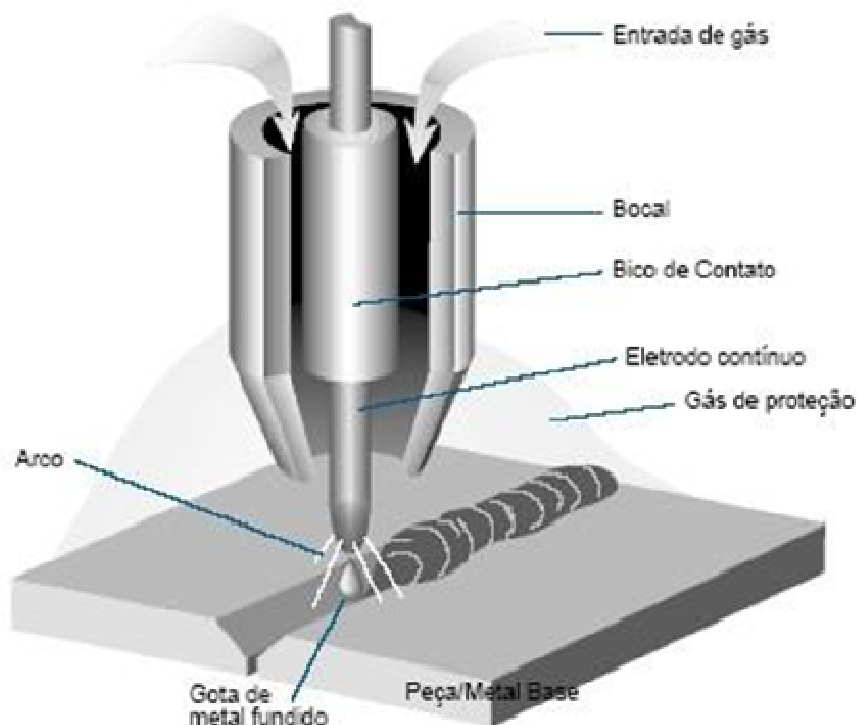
Soldagem GMAW (EBAH, 2013)
